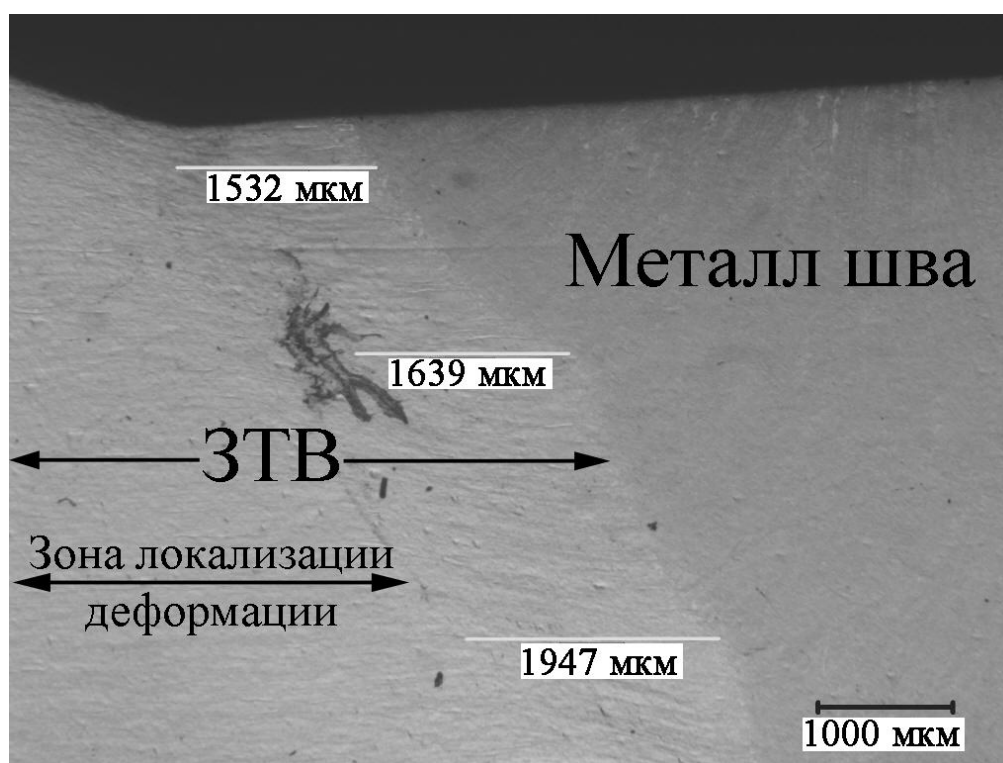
Зона пластической деформации симметричная относительно сварного шва месту разрушения.
